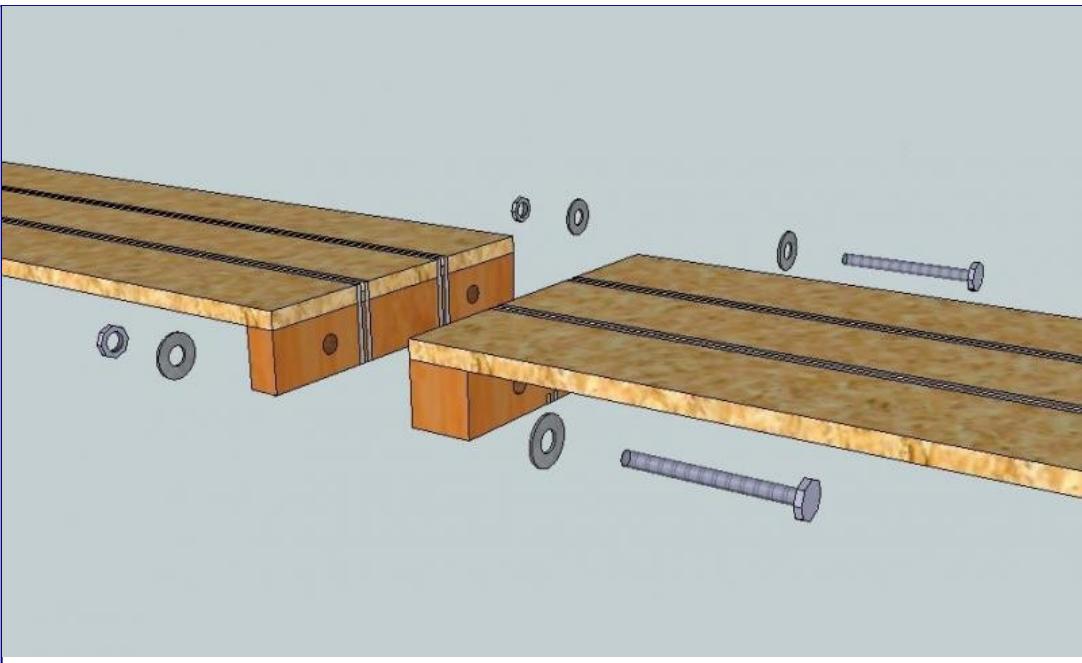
Assemblage de deux plaques de piste 2/2 [GSR_11]
